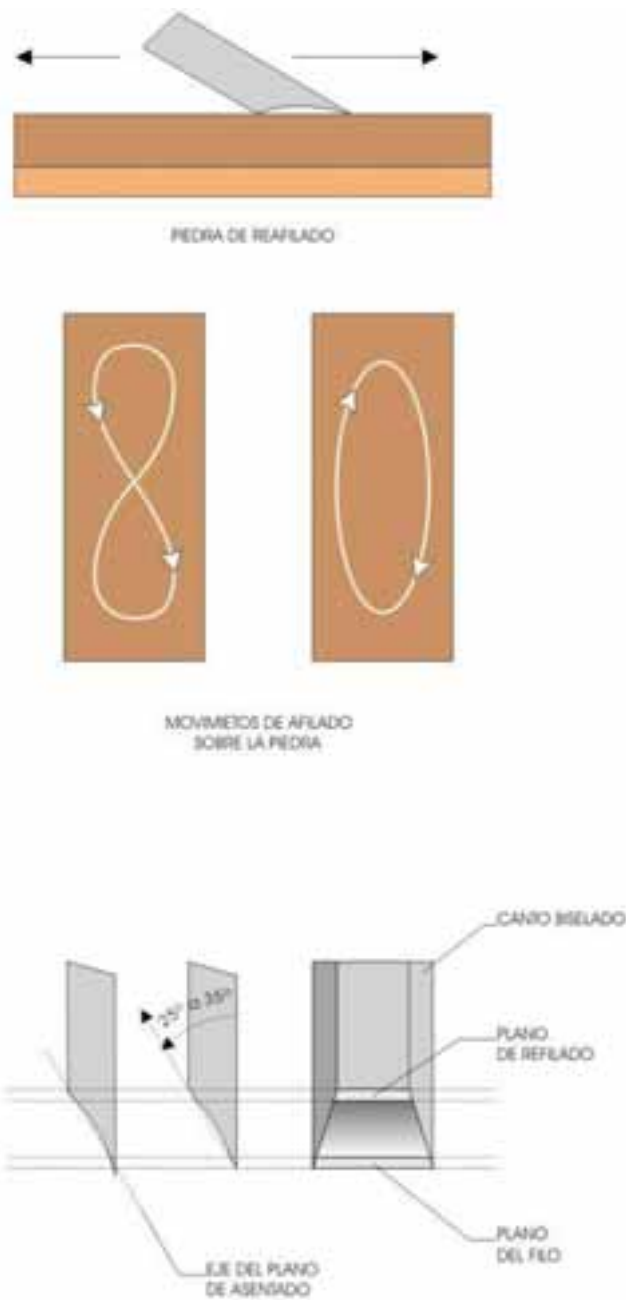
Colocación de la hoja sobre la piedra y movimientos de afilado. Representación de la forma correcta de refinado en el plano angulado por la muela.
